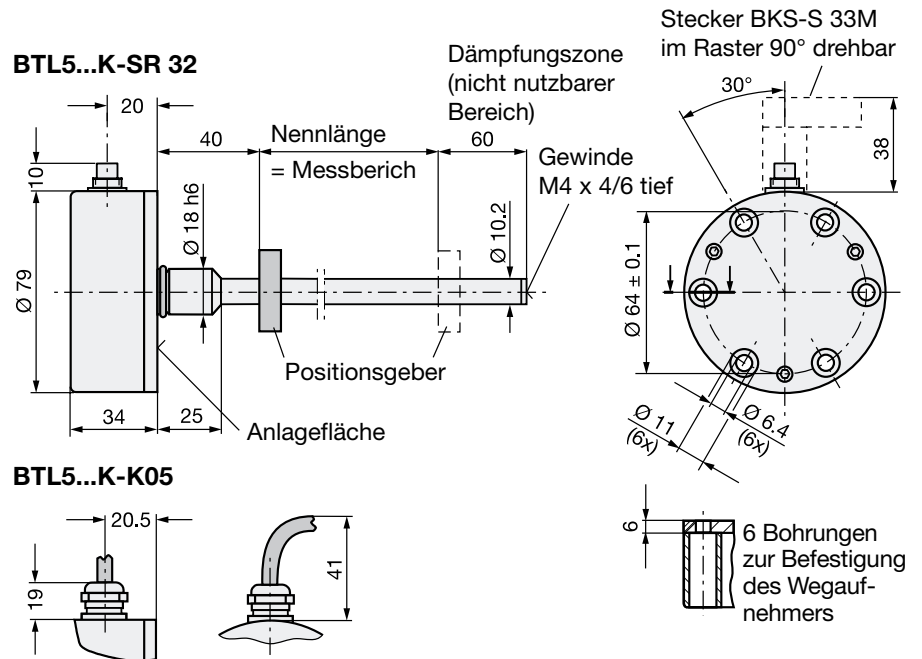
Wegaufnehmer BTL5...K..., Maßzeichnung
